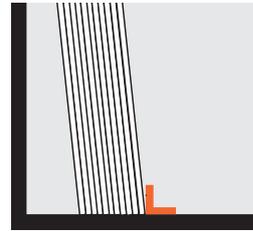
i resti di lamiera appoggiati alle pareti possono essere stabilizzati con un ferro ad angolo fissato al suolo.
